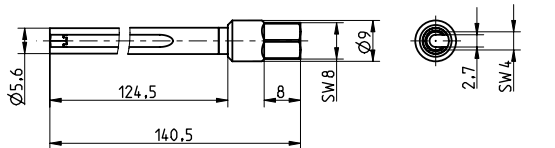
Montageschlüssel ø5,6 mm, geschlitzt, Typ 1300B14
